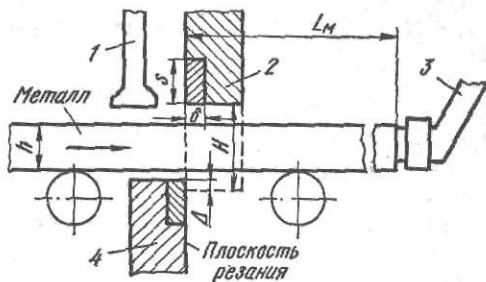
Схема резания металла на ножницах с параллельными ножами:
